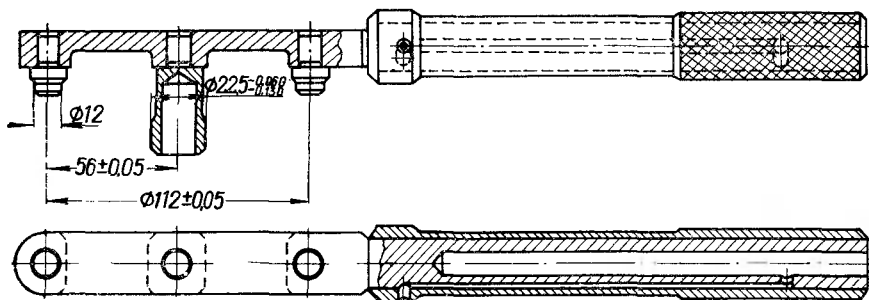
Ключ для отвертывания и заворачивания корпуса автоматической муфты опережения впрыска топлива
